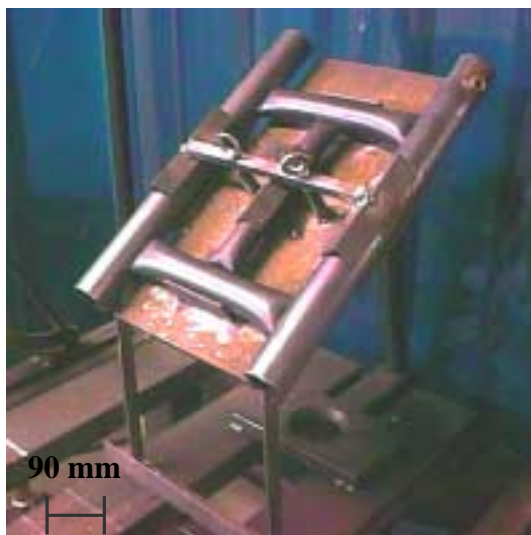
Foto mostrando o mini-gabarito com o protótipo posicionado para ser soldado.
